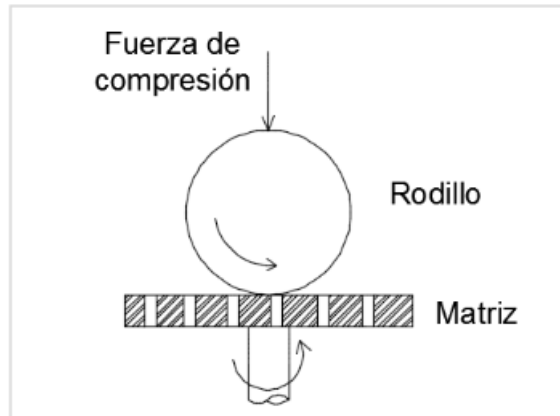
Sistema de compresión y extrusión por rodillos [34].
